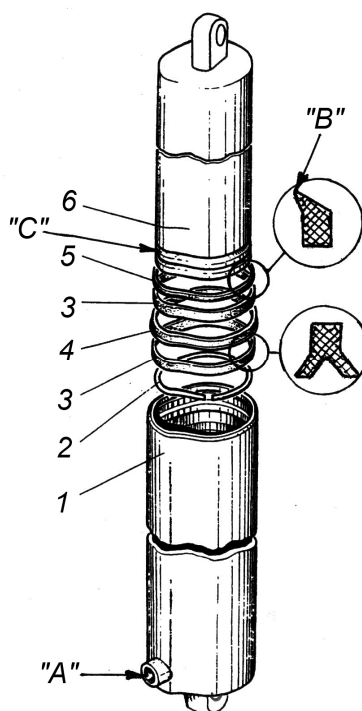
Гидравлический плунжерный гидроцилиндр:
